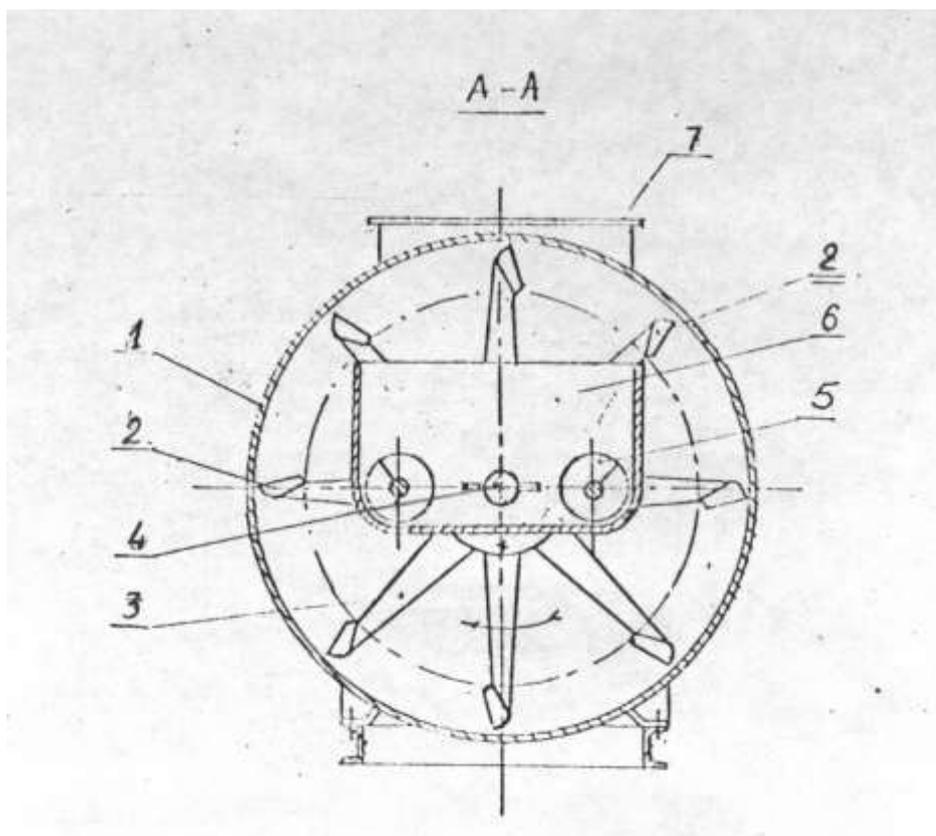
Схема устройства ковшового питателя роторного типа:
